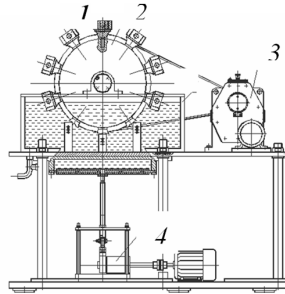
Установка для промивання від стружки порожнини корпусу газового лічильника: 1 – деталь; 2 – диск; 3 – привод; 4 – вібропривод
